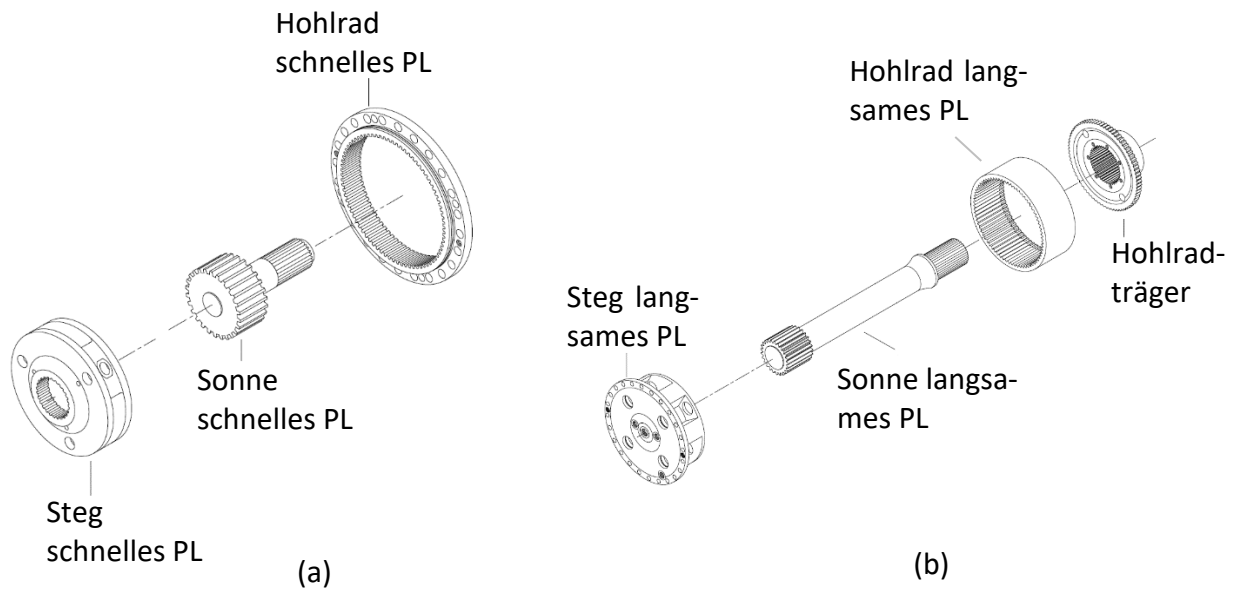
Explosionszeichnung des inneren (a) und äußeren (b) Planetengetriebes.
